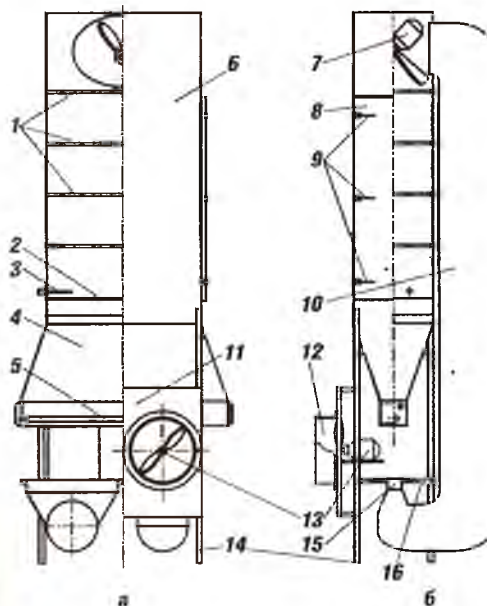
Схема сушильной установки: а — вид сбоку; б — вид спереди
